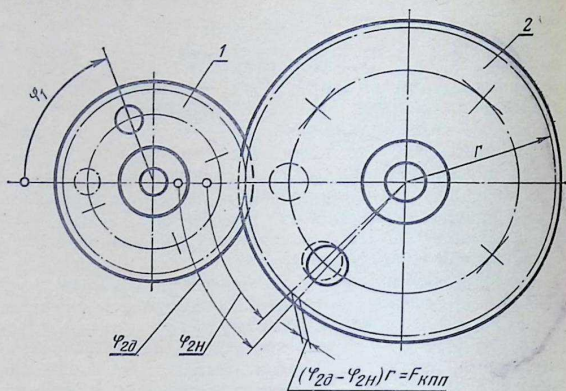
Определение кинематической погрешности зубчатой передачи:
